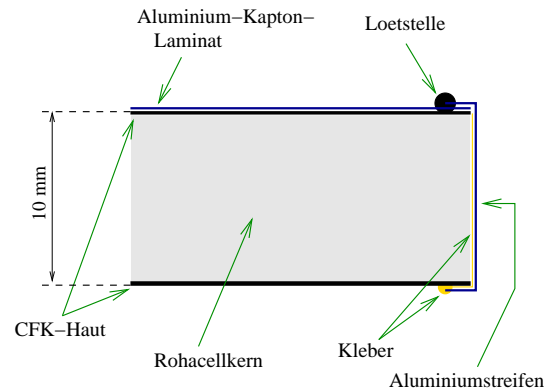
Skizzierter Querschnitt durch Modulplatte. Über die Kante der Platte (rechts) ist ein Aluminiumstreifen geklebt. Er wird auf der späteren Innenseite (oben) mit Ultraschalltechnik mit dem Aluminium-Kapton-Laminat verlötet.
